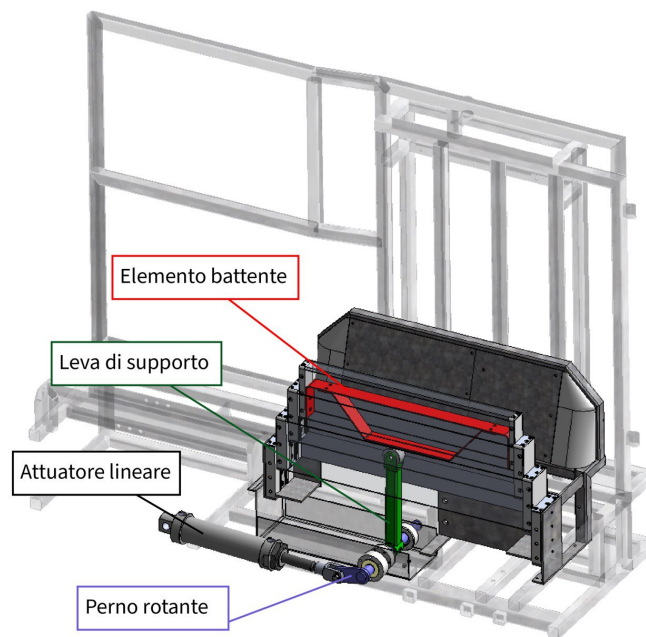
Parete centrale durante la fase di ingresso dell'animale
